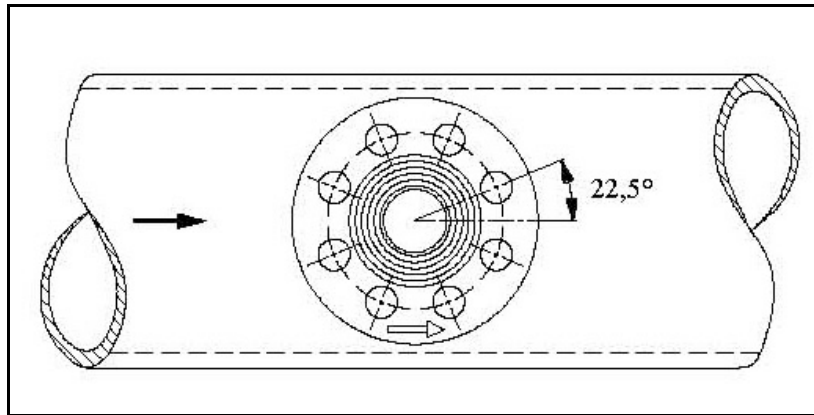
Montage eines Montagestutzens mit Flansch mit 8 Schraubenlöchern
